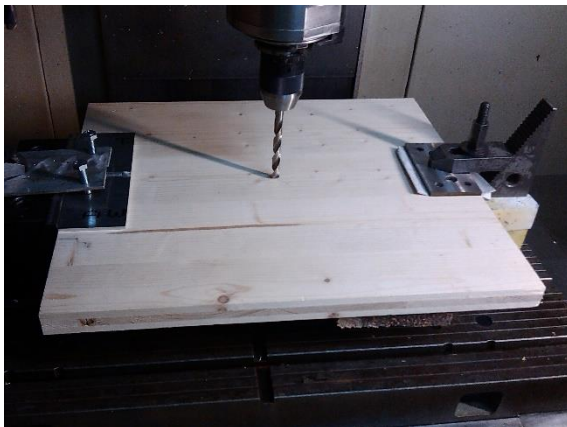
Colocação de 1/4 de placa de teto na máquina CNC e início da maquinação, LTM.
